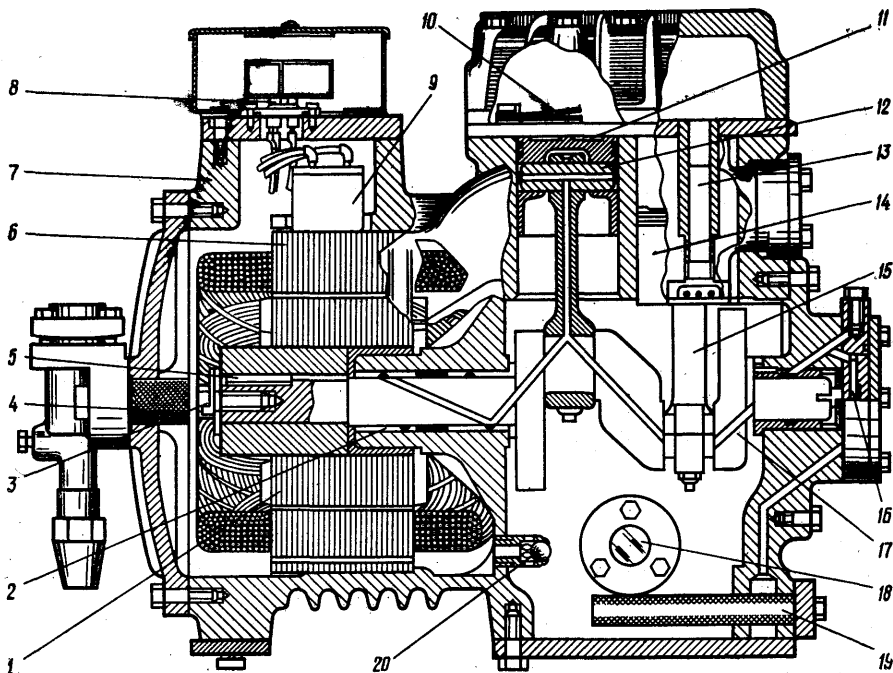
Разрез бессальникового двухцилиндрового компрессора:
